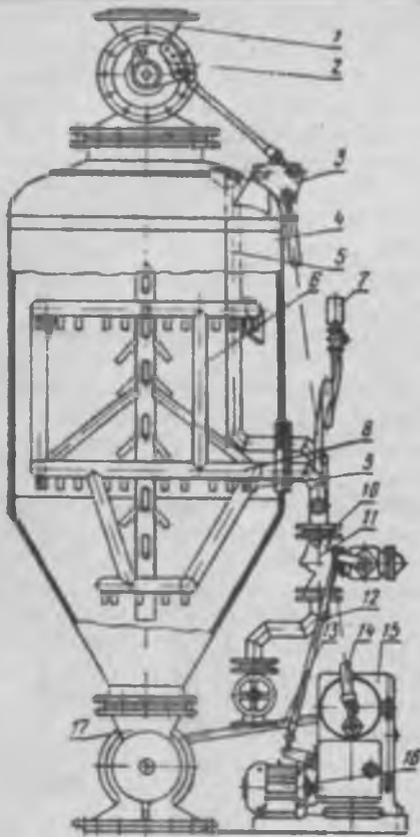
Пропариватель конструкции Г. С. Неруша:
